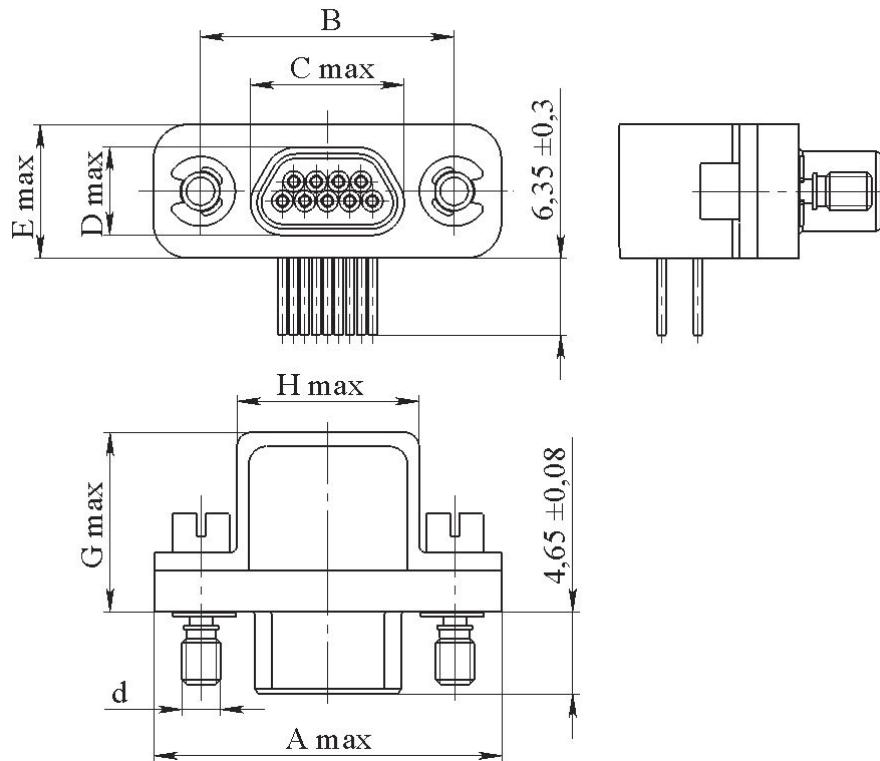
Соединитель СП397-4...Ш212В6С2
